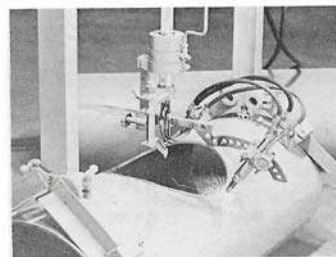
Machine portable pour l'usinage des piquages de tubes ou sur réservoirs.
